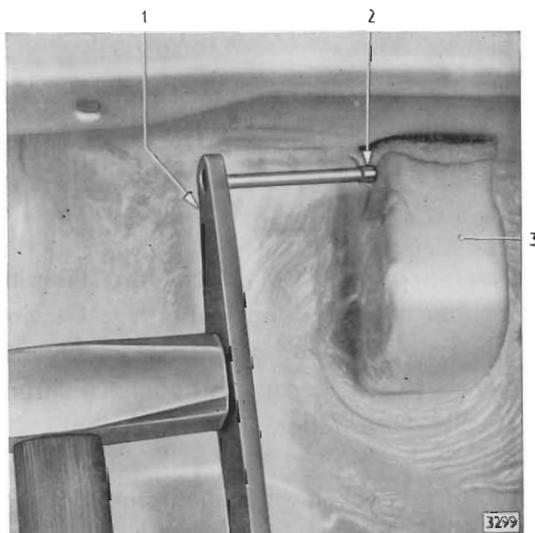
Scharnierspannhülse mit Werkzeug SW-361 herausschlagen
